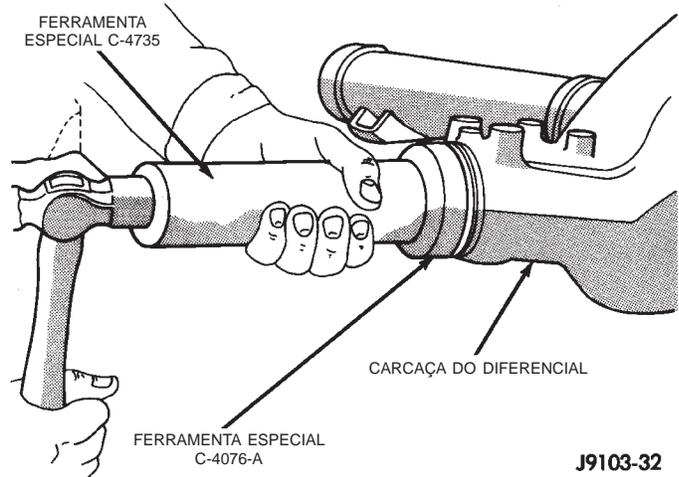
Instalação da Tampa do Rolamento Dianteiro do Pinhão
